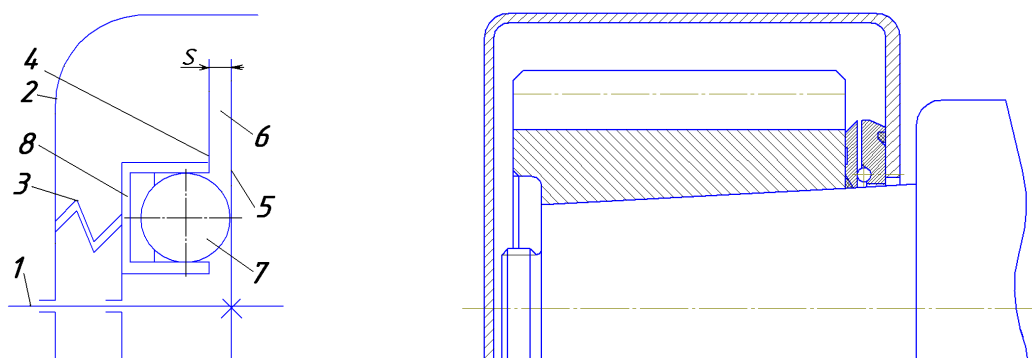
Схемное решение (а) и конструктивное исполнение (б) уплотнения выходного вала: 1 – вал; 2 – корпус; 3 – статическое уплотнение; 4 – неподвижная поверхность; 5 – подвижная поверхность; 6 – щелевое уплотнение; 7 – тела качения; 8 – подкладка регулировочная.
